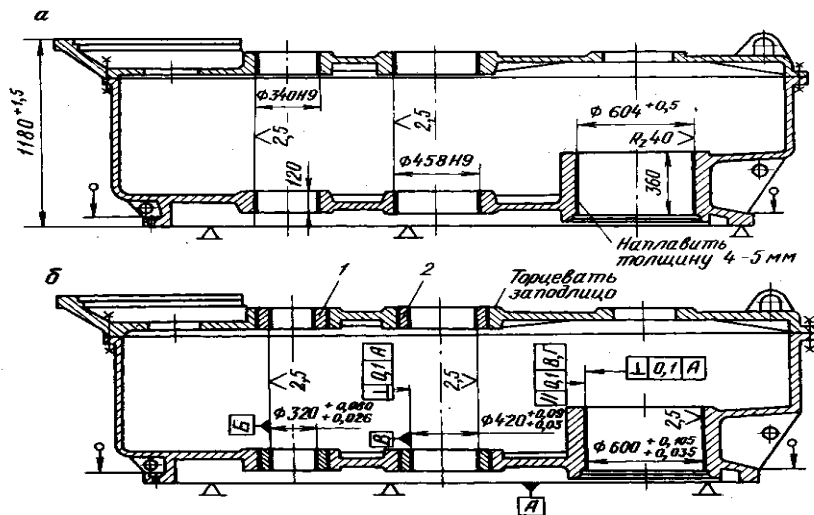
Ремонтные чертежи редуктора поворотного механизма экскаватора ЭШ-10/70 А
